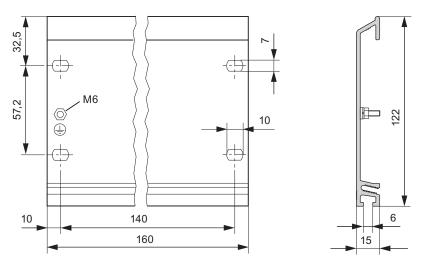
Plan d'encombrement du profilé support de longueur standard 160 mm
